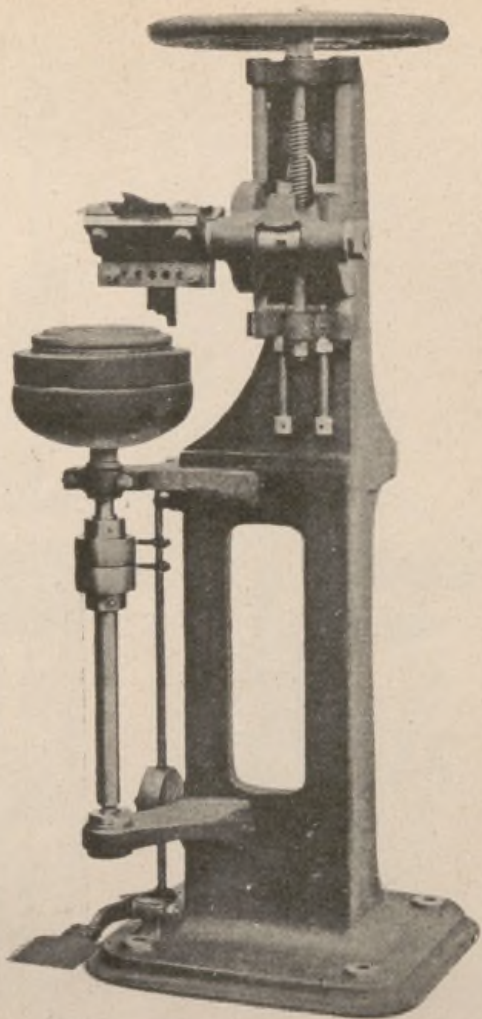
Machine pour la fabrication des moules (*Faure, à Limoges*).
